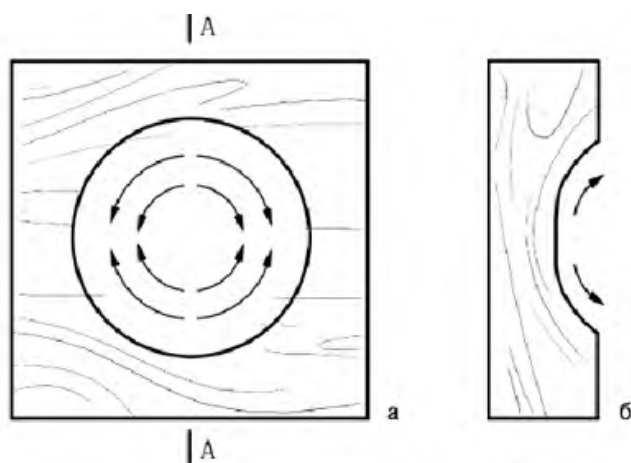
Выполнение круглой вогнутой выемки на торце заготовки первым способом (стрелками показано направление движения инструмента)
